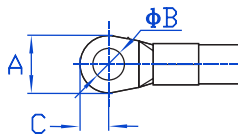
Dimensiones del terminal de cableado del UPS-IND HF 1300 M1
